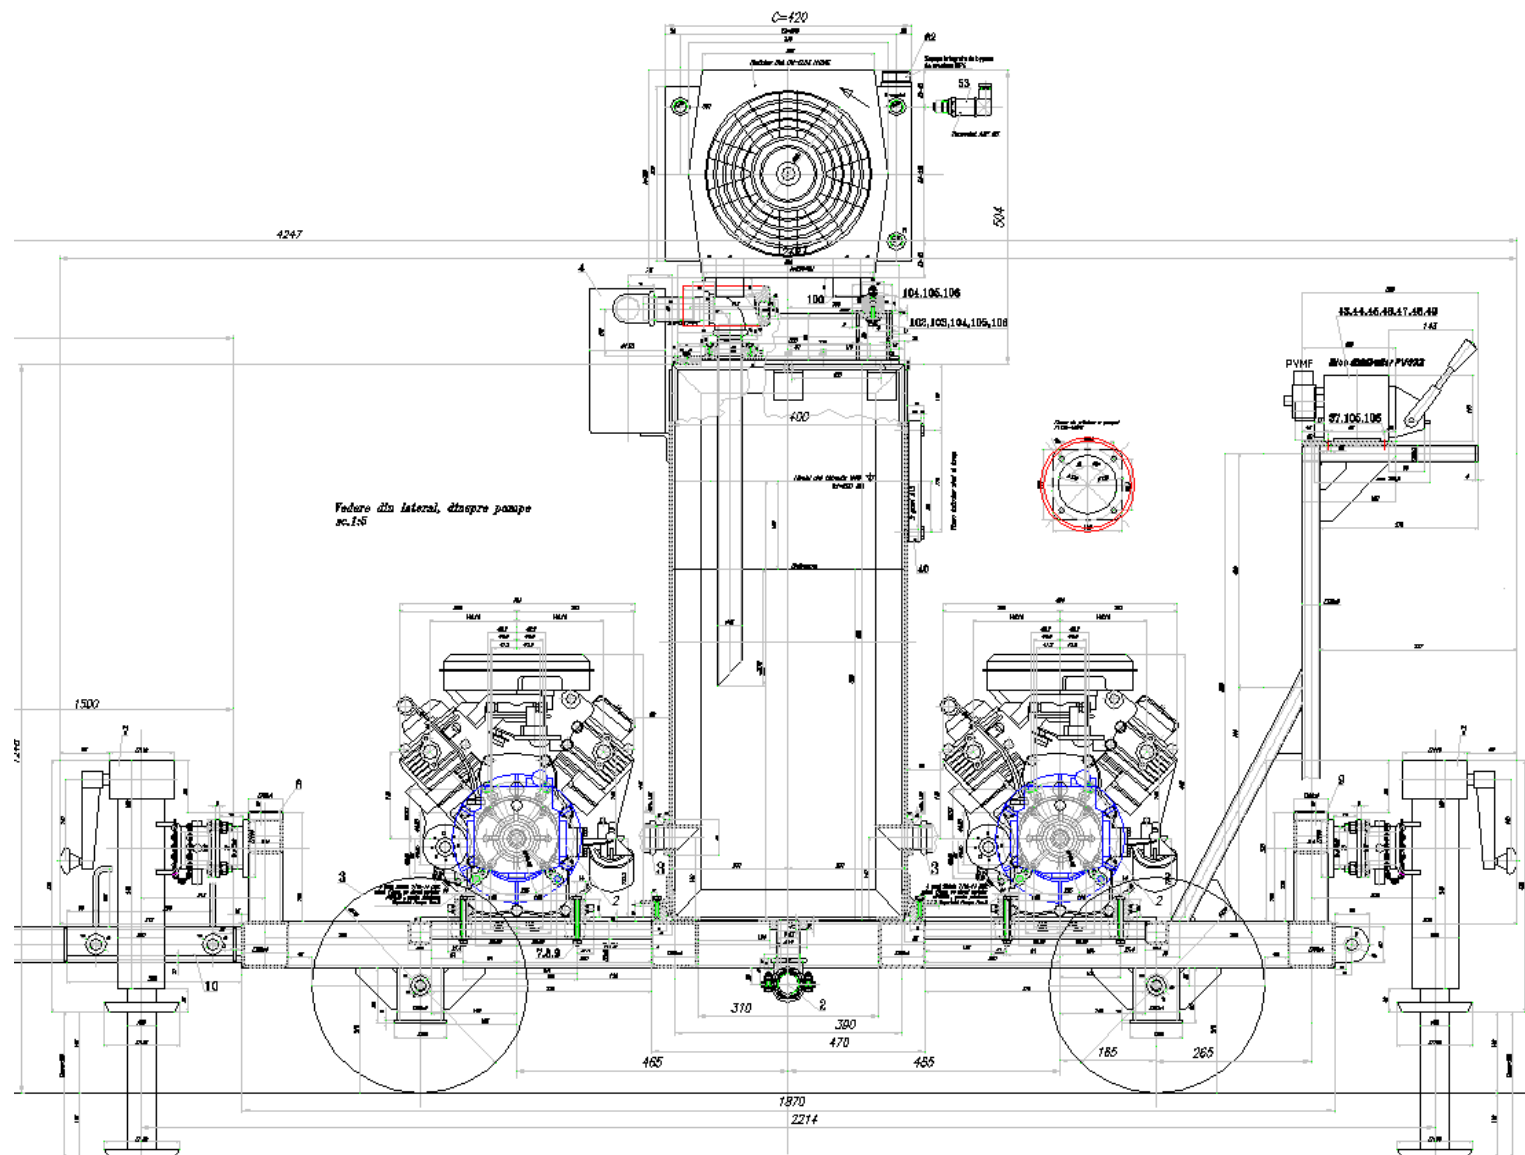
Desenul instalației de acționare hidraulică FG40, Grupul modular de presiune hidraulică FG40, vedere din lateral, dinspre pompe
